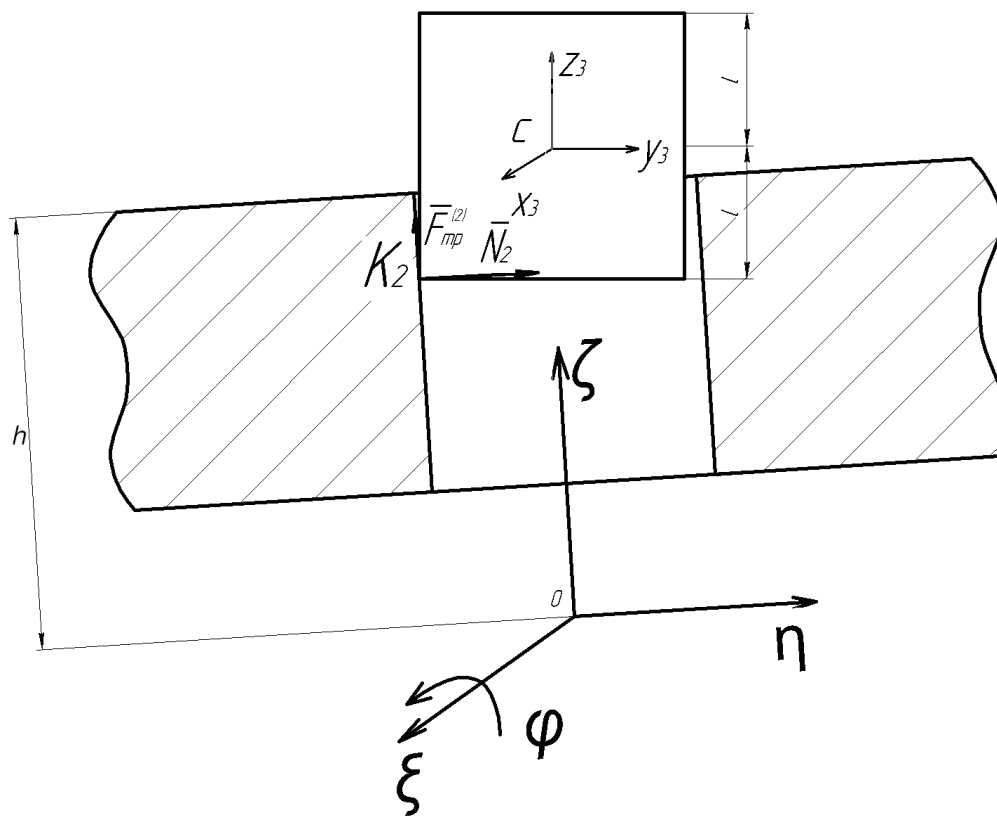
Расчетная схема одноточечного контакта торца вала и образующей втулки.
